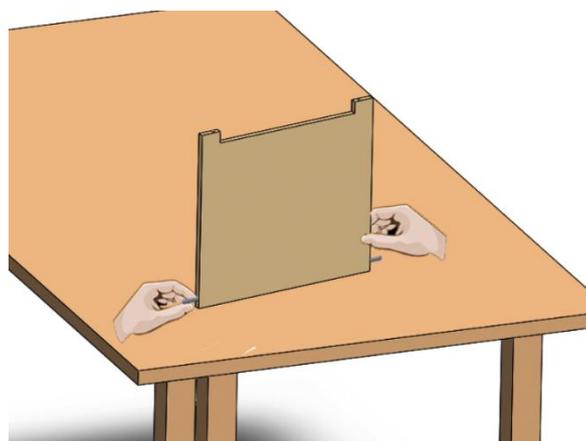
Paso 15 del ensamblaje del cajón (conjunto 2)
